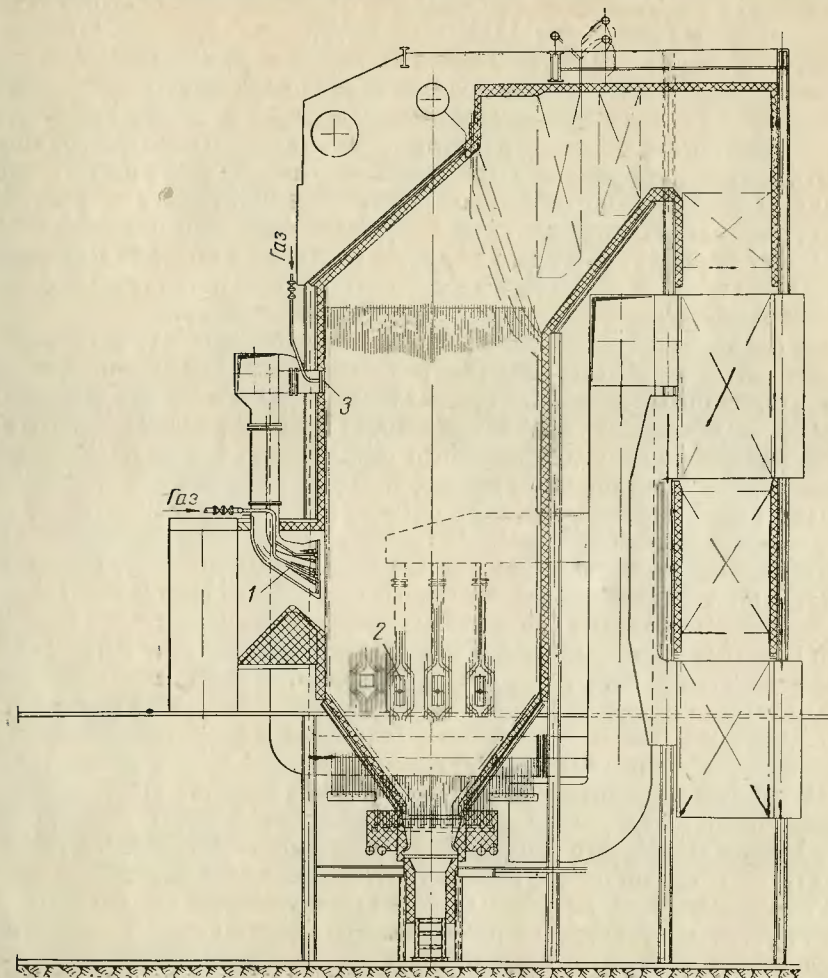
Компонировка горелочных устройств котлоагрегата ТП-170.
